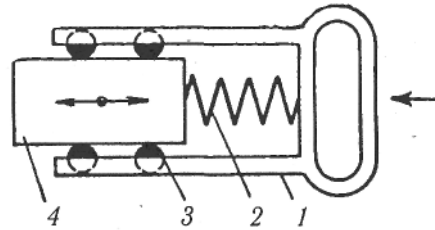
Віброізолюваний держак: 1 – держак; 2 – пружина; 3 – підшипник; 4 – корпус
